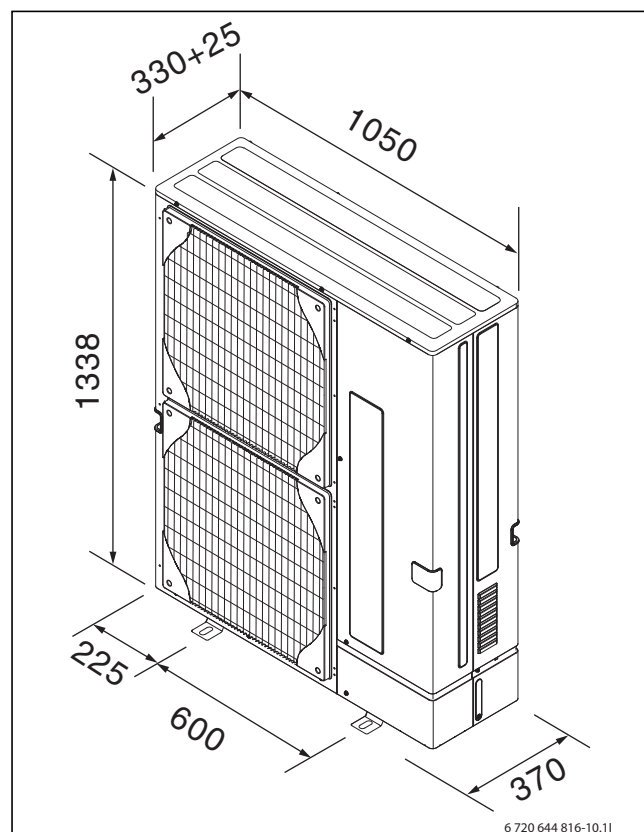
Dimensioni unità esterna ODU 10, 11s, 11t, 12s e 12t (misure in mm)
